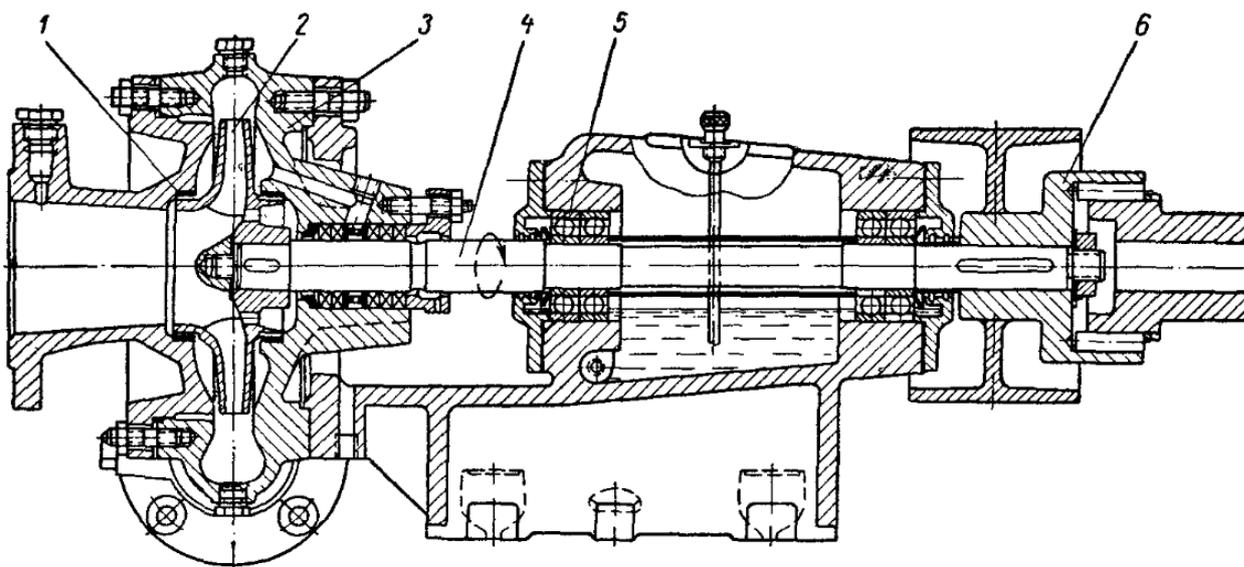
Консольный одноступенчатый центробежный насос:
